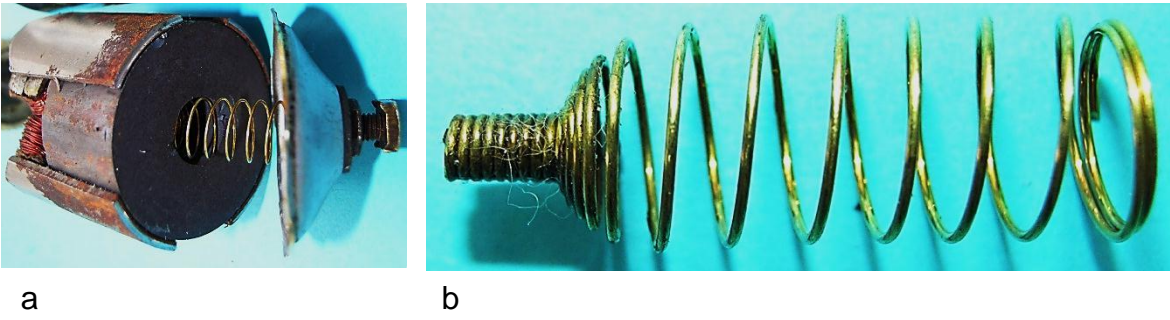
Federkontakt: a) Schleifkontakt innerhalb der Bohrung des Magneten, b) Kontaktfeder
